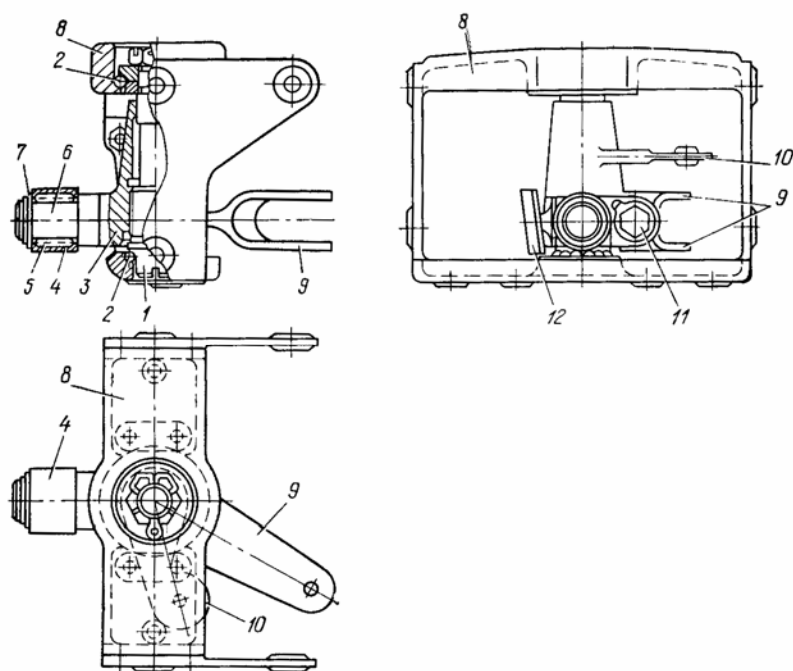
Замок входной двери: 1—ось рычага; 2—шариковый подшипник; 3—рычаг; кролик рычага; 5—игольчатый подшипник; 6—палец рычага; 7—шайба; 8—корпус; 9—вилка рычага; 10—ушко рычага; 11—стяжной болт; 12—щиток
